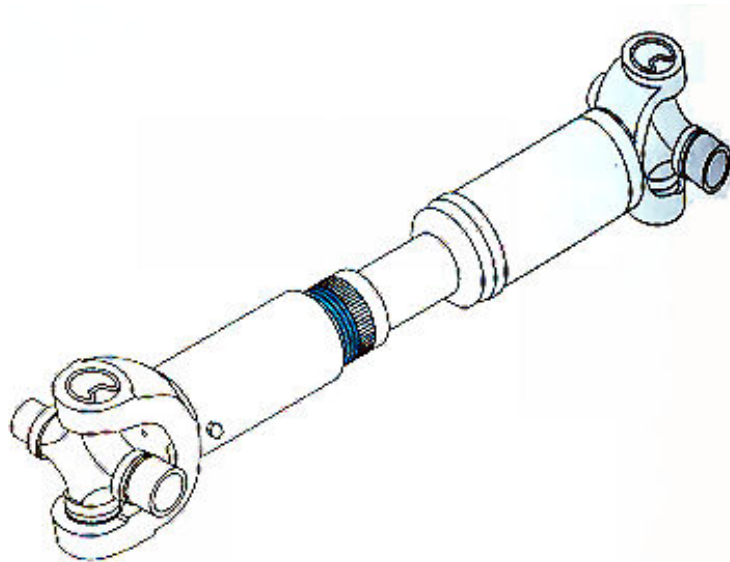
Junta Universal. Também conhecida por junta Cardan.
